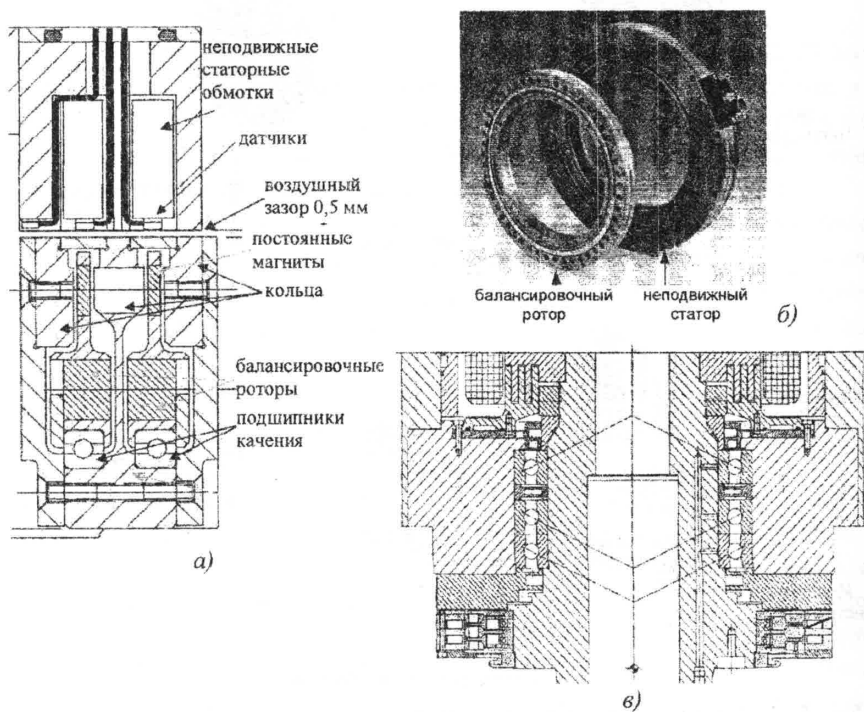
Конструктивное исполнение балансировочного устройства (а), его общий вид (б) и установка на шпиндельный узел станка (в)
